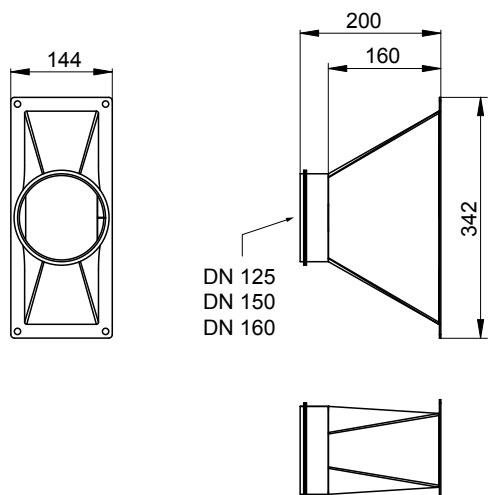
Dimensions des raccords de transition 1 kg/h (dimensions en mm)
